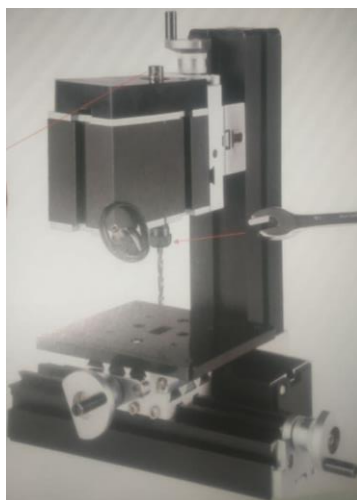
Координатно-розточне компонування для обробки металу та дерева
